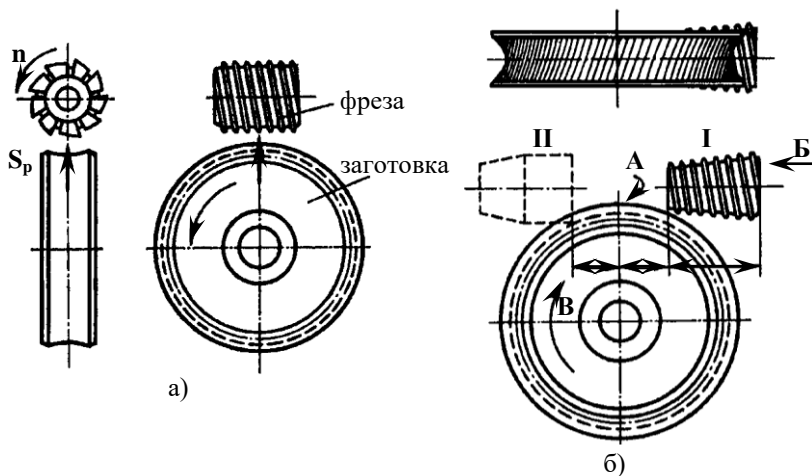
Нарізання зубів черв'ячних зубчастих коліс черв'ячними фрезами:
